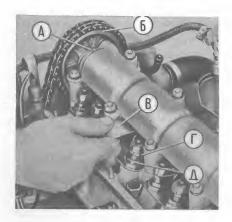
Регулировка распределительного механизма: А и Б — установочные метни распределительного вала; В — щул толщиной 0.15 мм для проверки зазора;  $\Gamma$  — шестигранник регулировочного болта; Д — контргайка.
